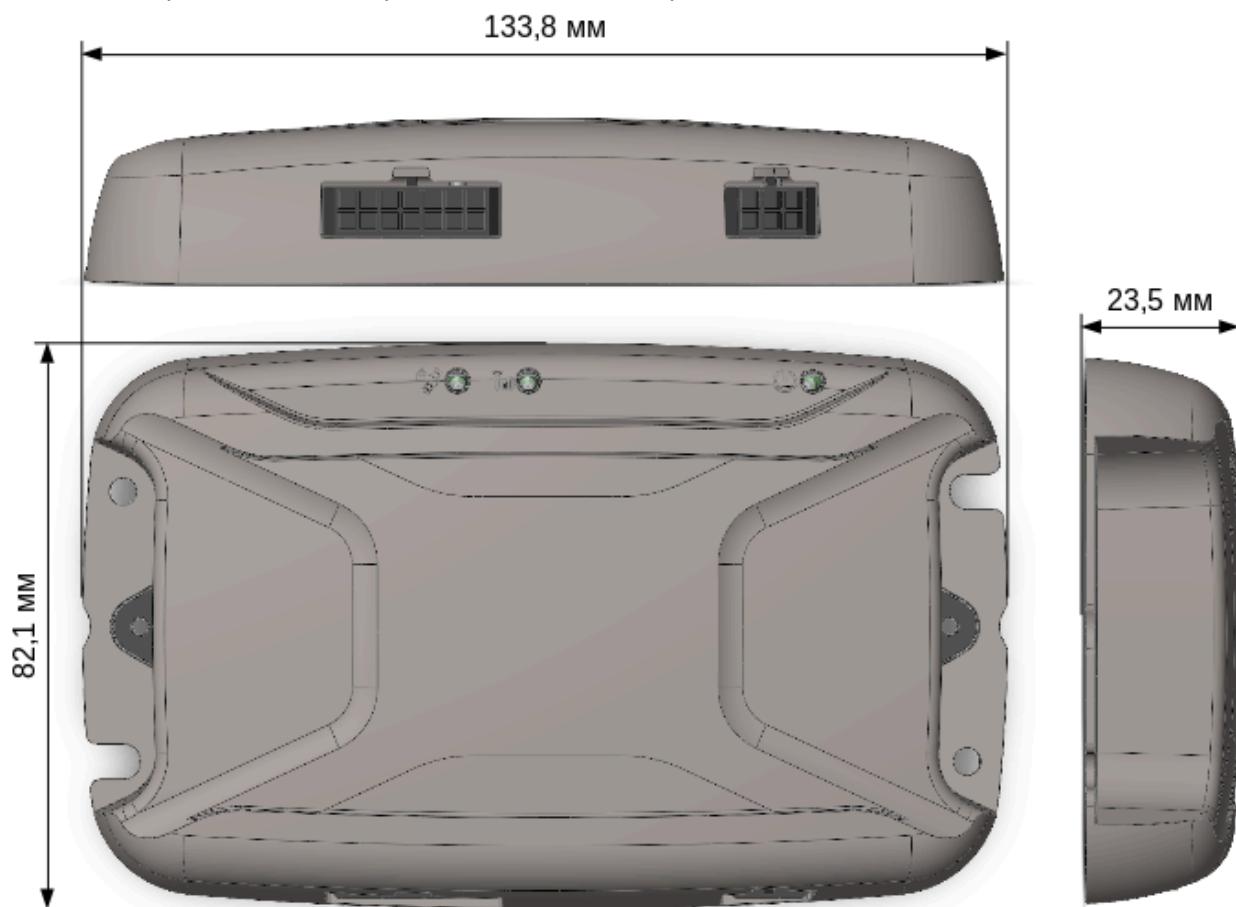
Внешний вид корпуса основного блока и габаритные размеры.
